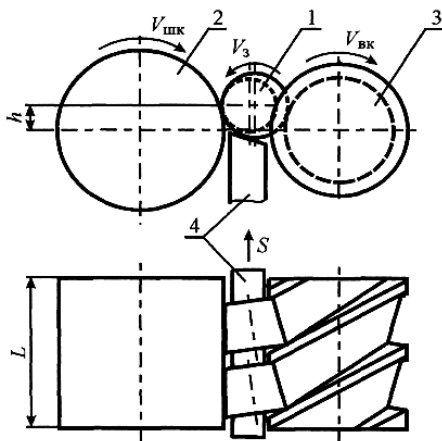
Схема безцентрового шліфування конічних поверхонь
